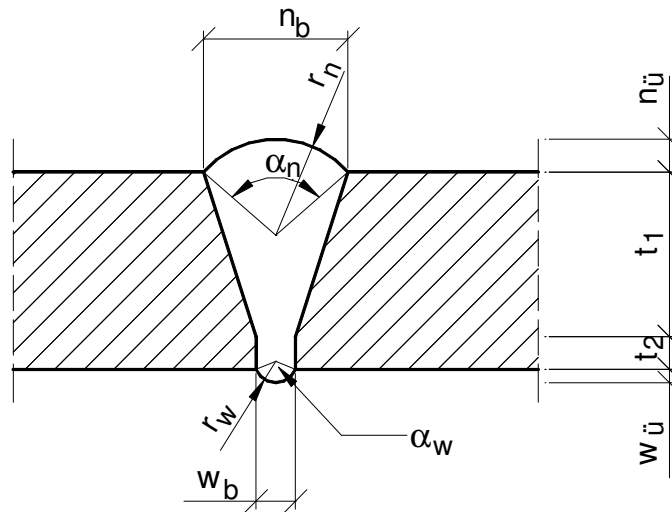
Geometrie des Schweißspaltes
